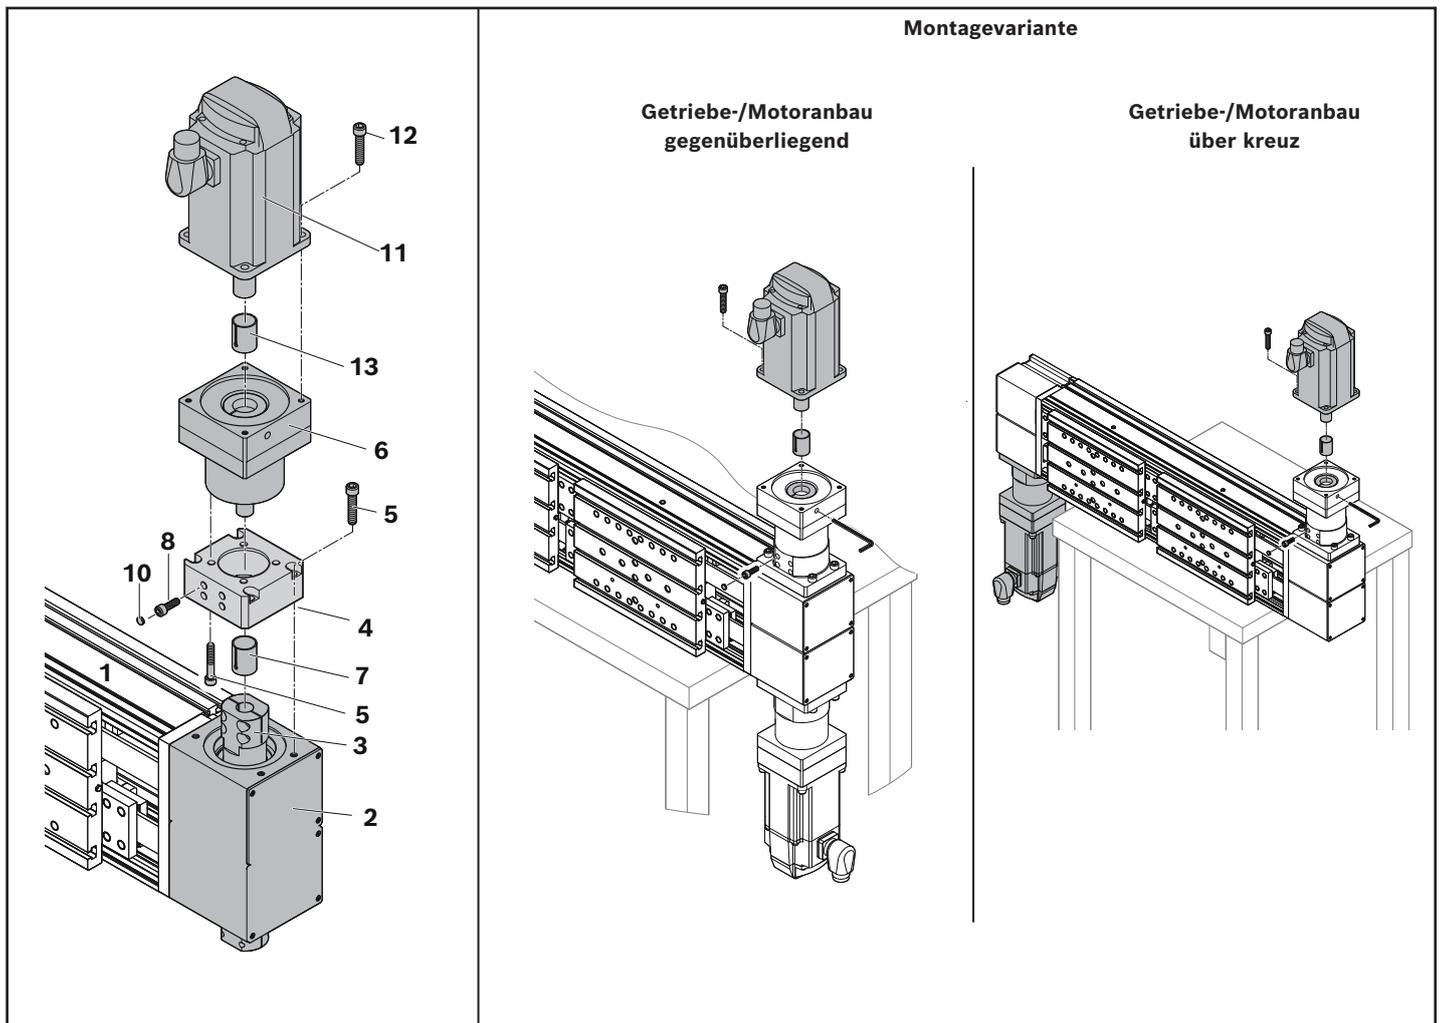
Getriebe-/Motoranbau CKR-280-DB
